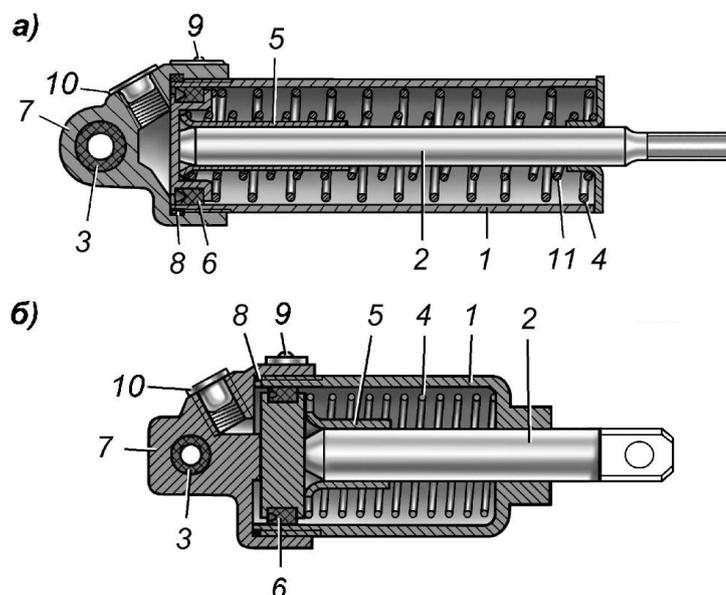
Пневматические цилиндры привода заслонки механизма вспомогательной тормозной системы (а) и привода рычага останова двигателя (б):
